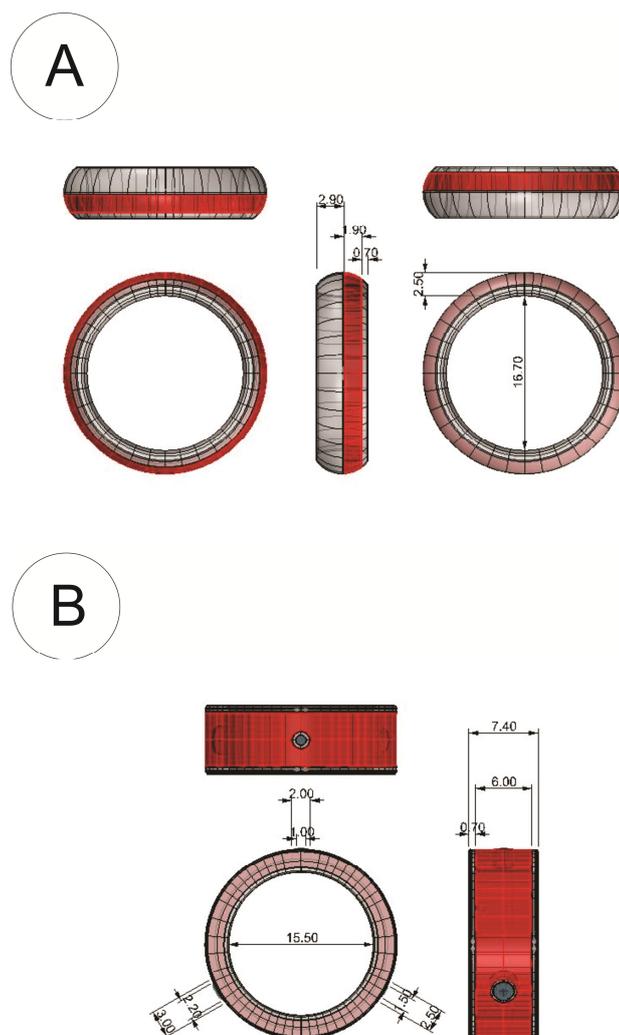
DESENHO TÉCNICO DAS ALTERNATIVAS ASPECTOS TÉCNICOS
